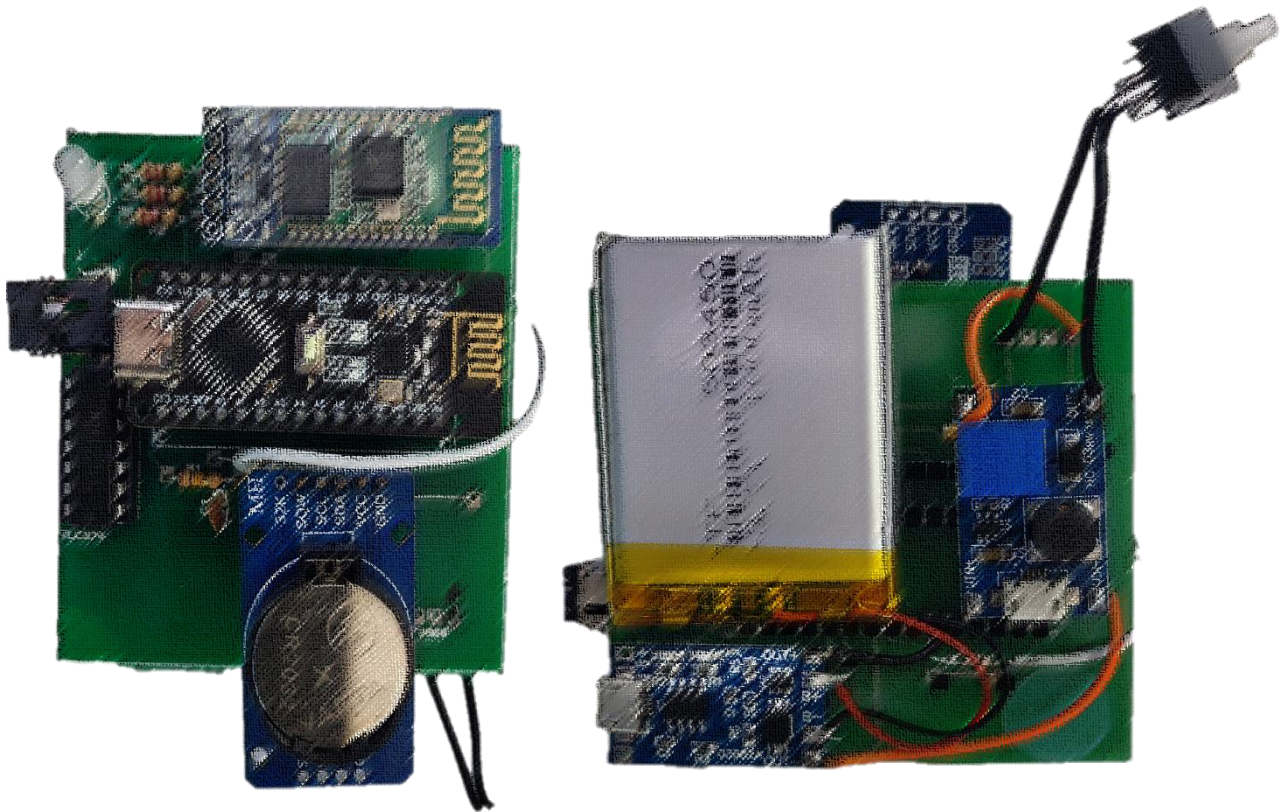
Carte PCB finale du glucomètre après assemblage des composants
